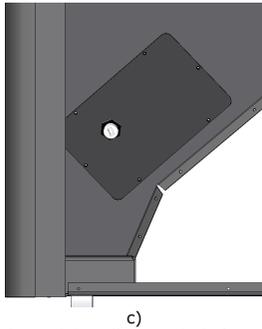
Colocación del sensor de nivel de pellets en el silo (instalación a la izquierda de la caldera)
